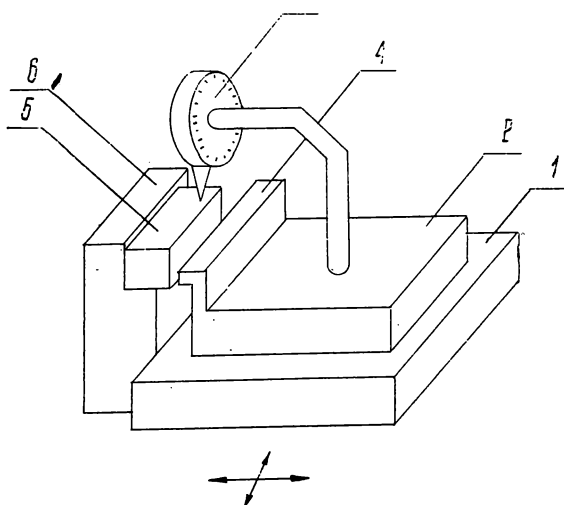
Схема устройства для формирования профиля ферритовых полублоков
